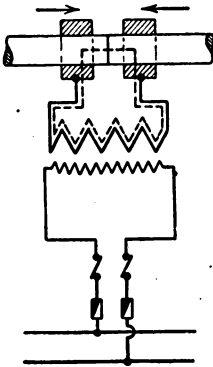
Elektrisches Stumpfschweißen.
